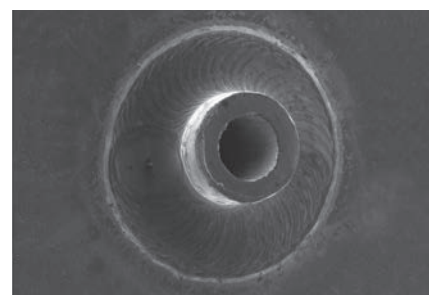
Beispiel für Laserschweißung einer Nickelfolie mit Hologramm
